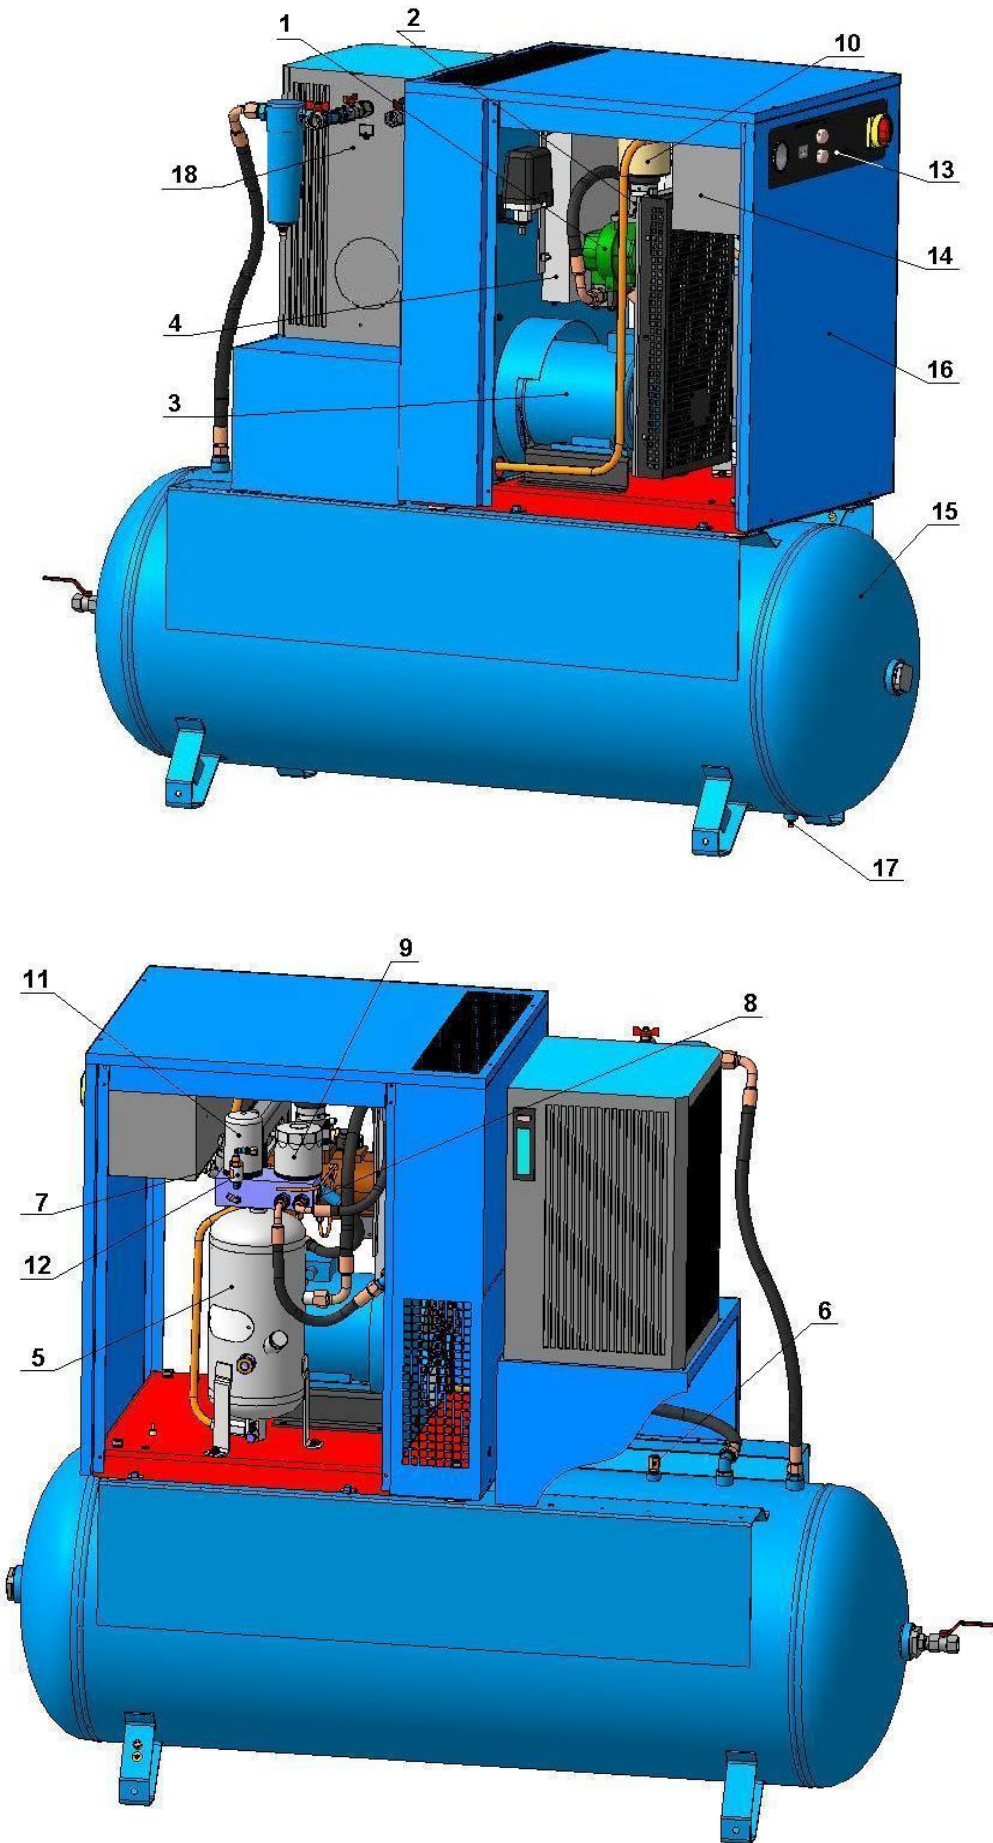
Общий вид компрессорной установки ВК5-...-500(Д), ВК7-...-500(Д), ВК10-...-500(Д)
